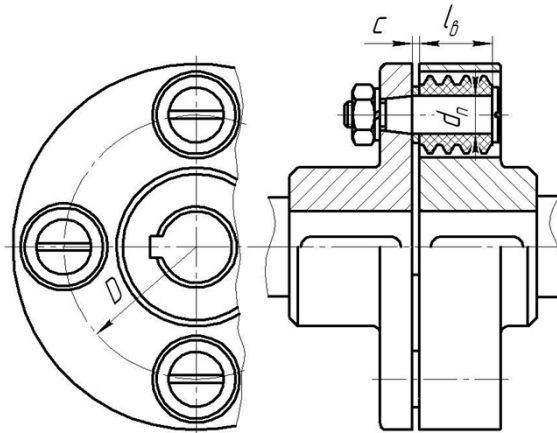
Розрахункова схема пружної втулково-пальцевої муфти
